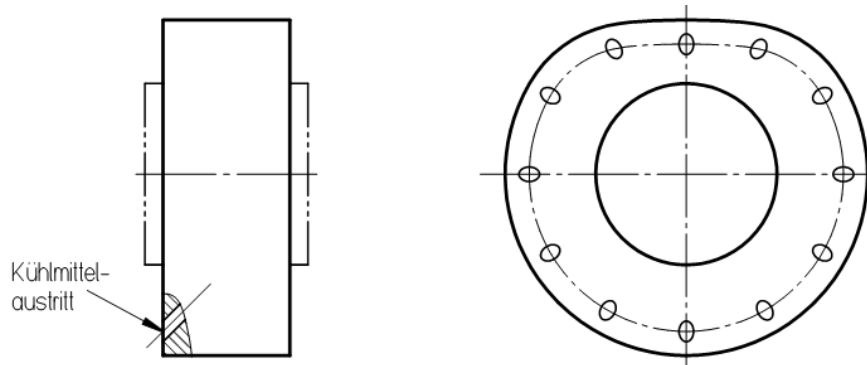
Unrunde Schleifscheibe mit Innenkühlung und planseitigem Kühlmittelaustritt
